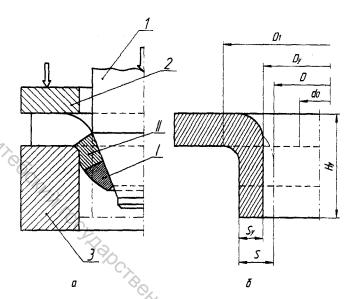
Отбортовка отверстий с утонением: a – очаг пластической деформации; б – геометрические размеры заготовки; 1 – пуансон; 2 – прижим; 3 - матрица; 1 - участок отбортовки без утонения стенок; II – участок отбортовки с утонением
